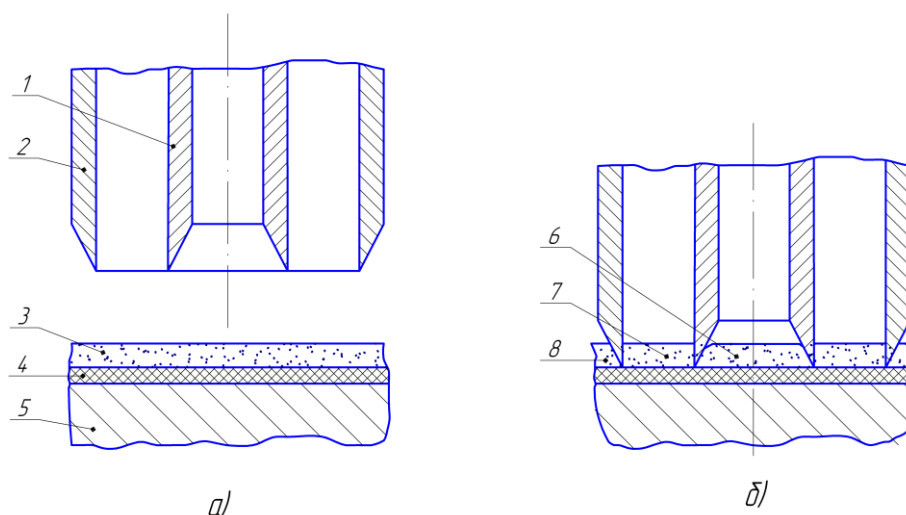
Схема высечки кольцевых заготовок абразивных кругов: а – исходное положение; б – в конце хода; 1,2 – режущие элементы; 3 – листовой прокат; 4 – подложка; 5 – стол; 6 – внутренняя высечка; 7 – кольцевая заготовка; 8 – наружный облой
